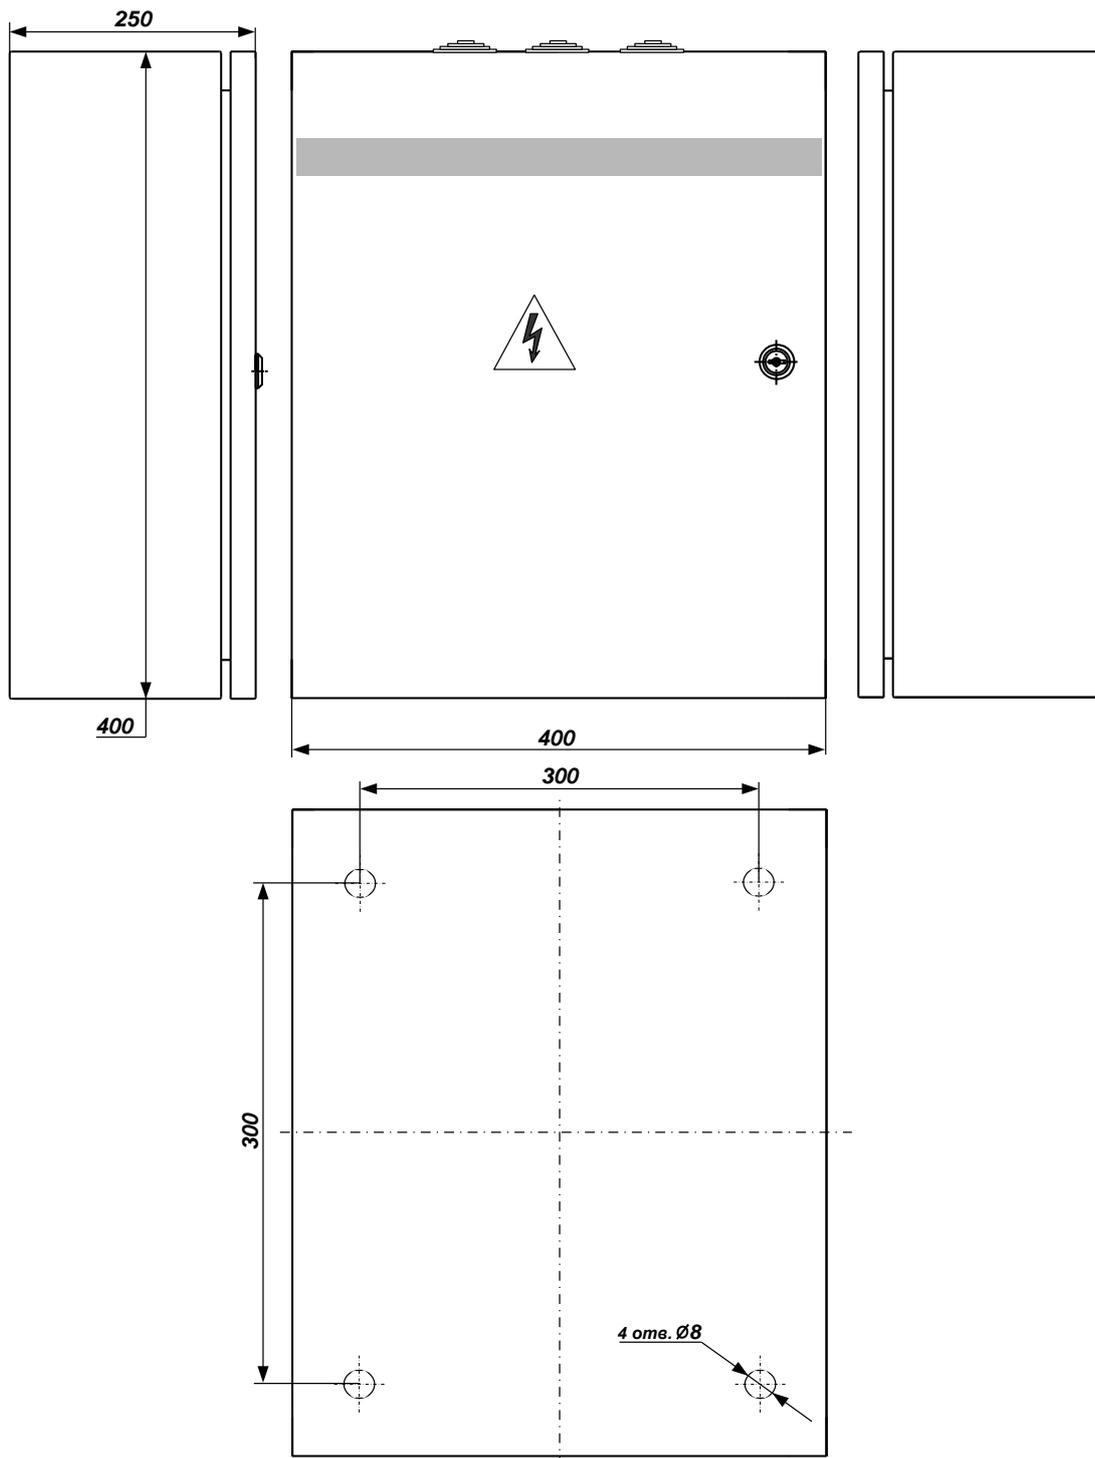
Внешний вид ППК-Р. Габаритные и присоединительные размеры
